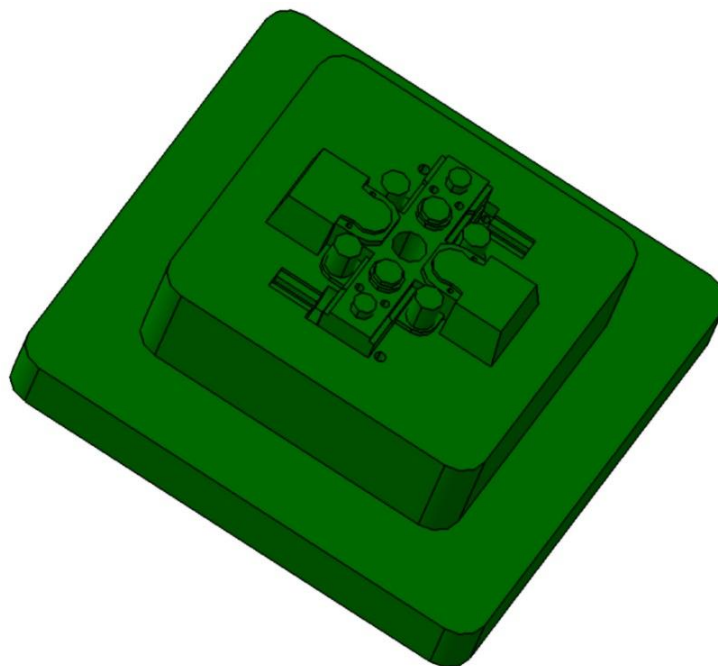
Rozvržení vyhazovačů ve tvárníku
